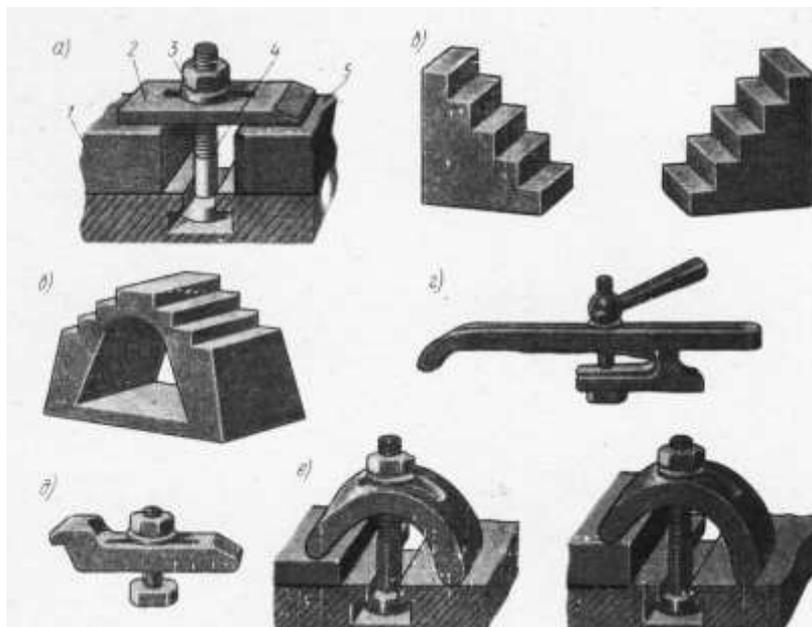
Вспомогательный инструмент для крепления приспособлений
